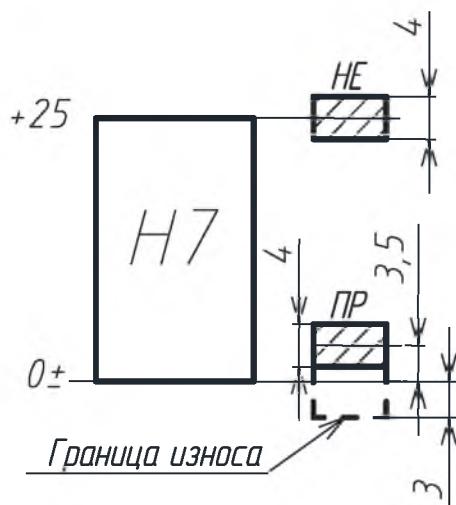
Схема расположения полей допусков рабочих калибров Ø40H7
